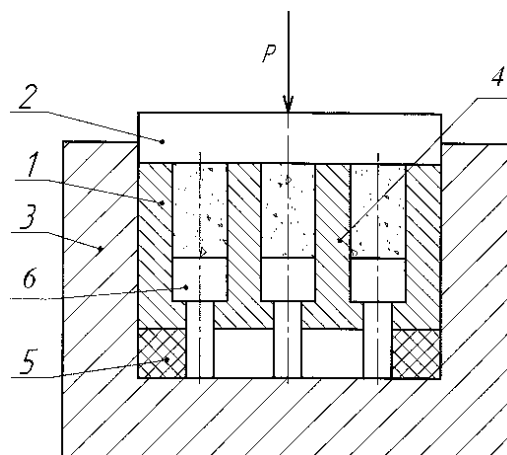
Многоместная пресс-форма для прессования порошков
